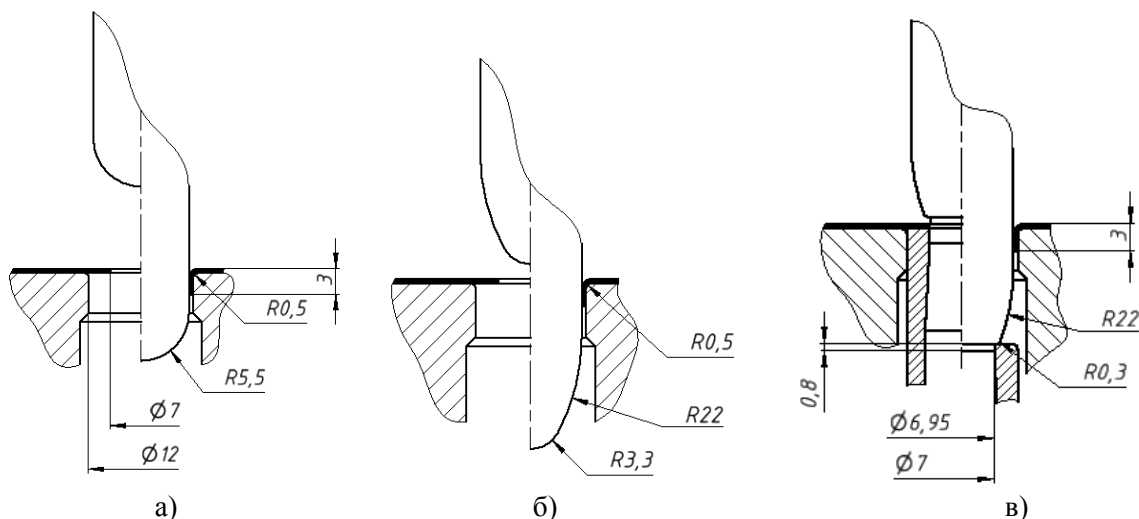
Варианты конструкций пуансонов: а) сферический пуансон; б) криволинейный пуансон; в) комбинированный пуансон с криволинейной образующей и пробивной кромкой
